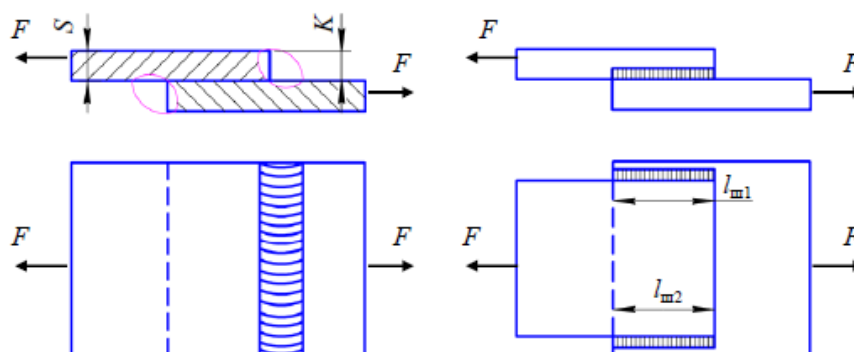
Свахлесточное сварное соединение
